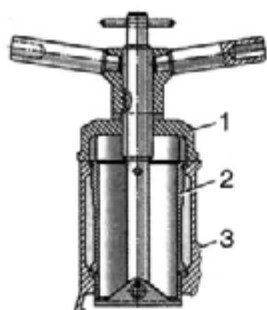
Съемник для выпрессовки гильзы из блока цилиндров:
